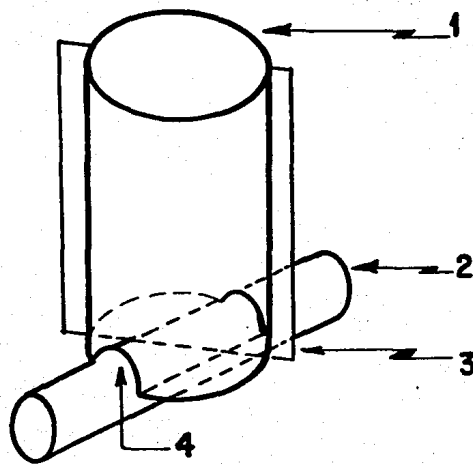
TANQUE PARA SOLDAR EN AGUA.
